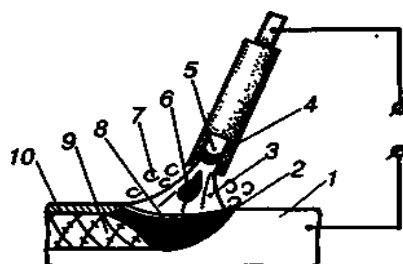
Схема ручной дуговой сварки плавящимся покрытым электродом
